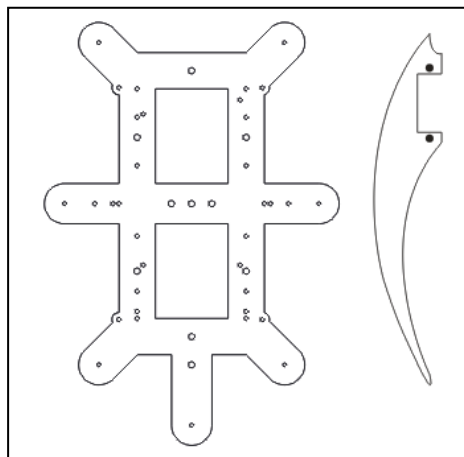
Diseño de CorelDraw del cuerpo y la Pata.
